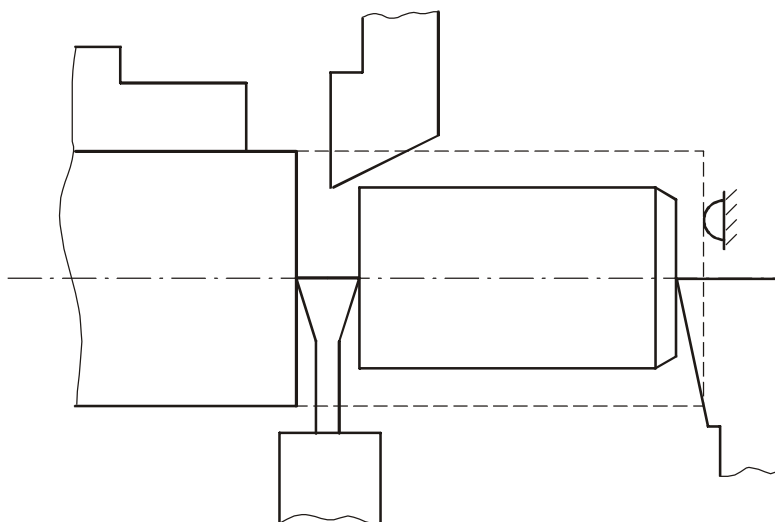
Схема токарно-револьверной операции обработки ролика (номинальный диаметр – 20 мм, длина – 30 мм)
